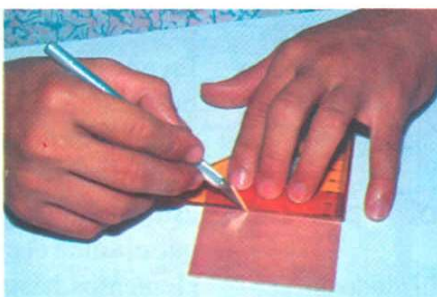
Para el corte de la plaqueta también se puede utilizar un bisturí
